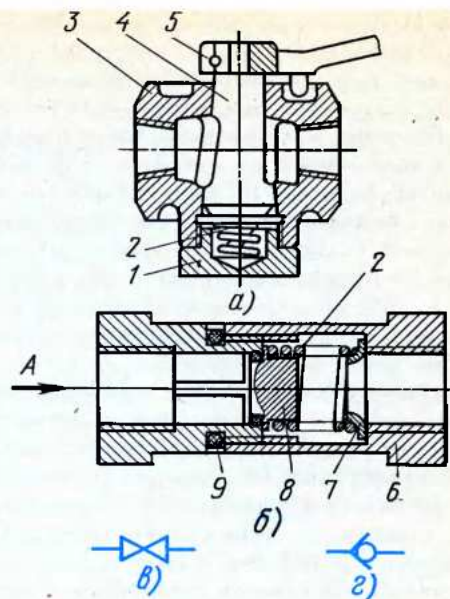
Разобщительный вентиль (а) и обратный пневмоклапан прямого действия (б) и их обозначения на пневмосхемах (в, з):
